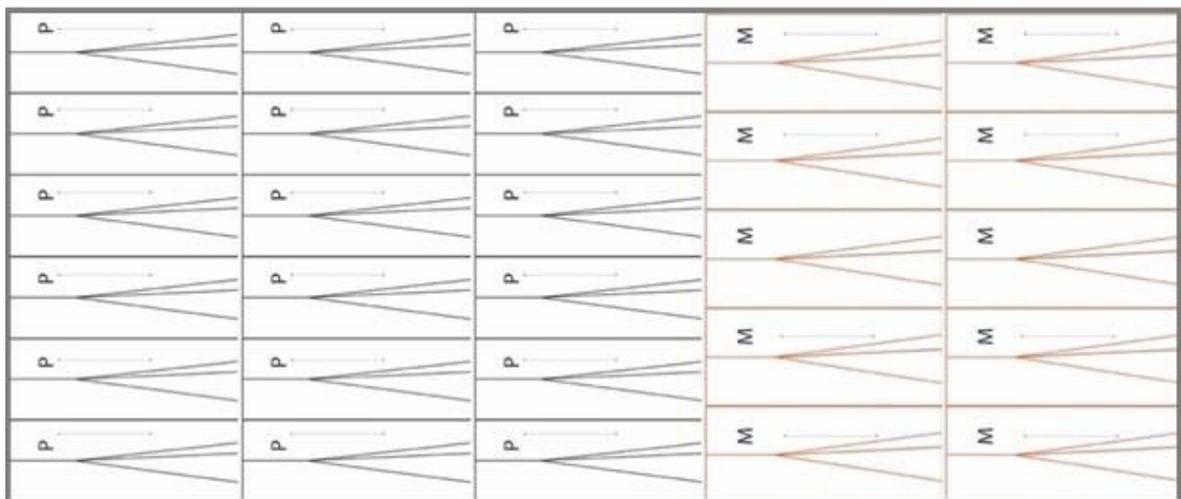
plano de corte em metragem ampla de tecido. Fonte: elaborado pelos autores.
